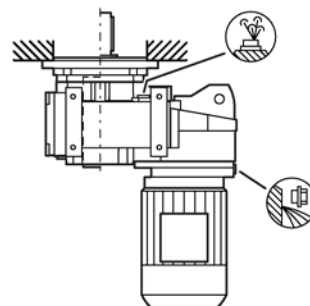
Монтажные положения для плоского редуктора F.AD в насадном исполнении, типоразмеры 39-189
